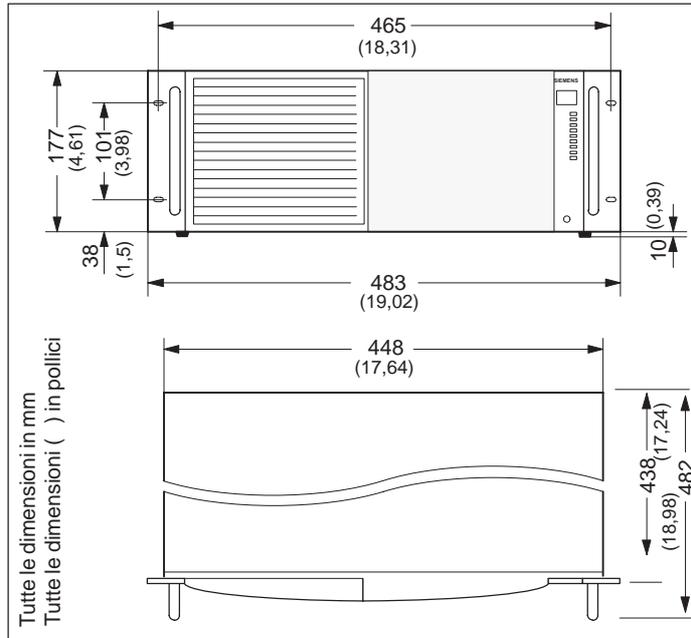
Dimensioni di montaggio del SIMATIC PC
